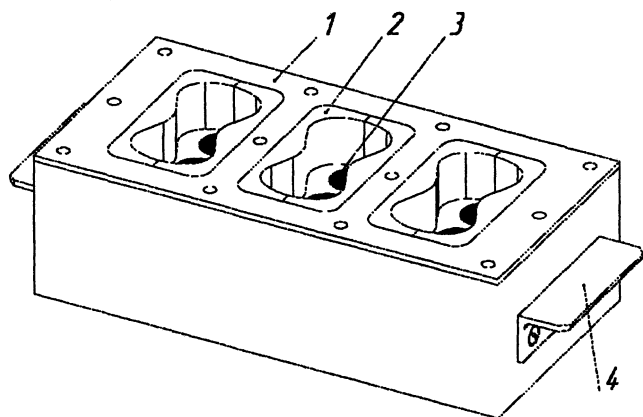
Ящик стержневой для изготовления стандартного образца «восьмерка»
